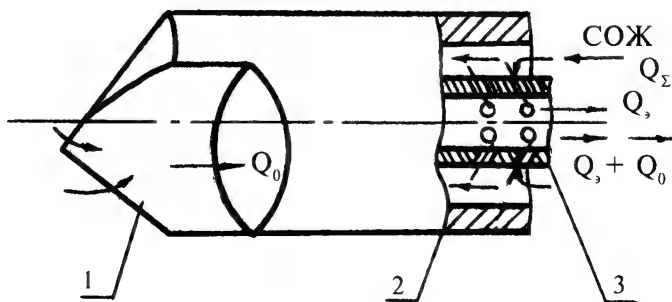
Эжекторное сверло: 1 - режущая часть, 2 - наружная трубка, 3 - внутренняя трубка
